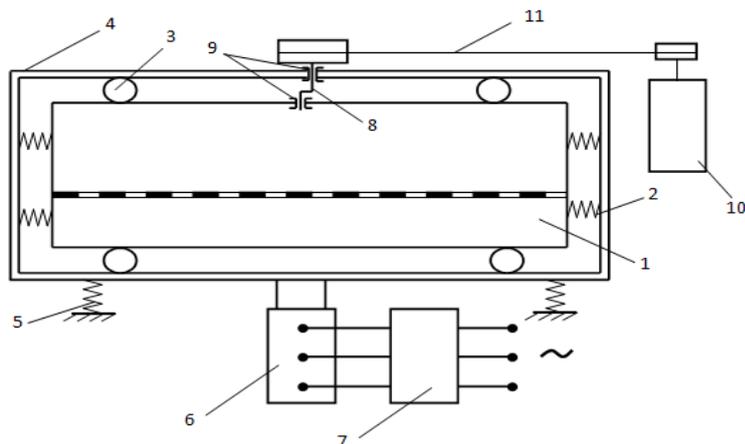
Новая конструкция вибрационного грохота: 1 - короб с просеивающей поверхностью; 2 - упругие элементы; 3 - кинематические соединения; 4 - подвижная рама; 5 - амортизатор; 6 - вибропривод; 7 - преобразователь частоты; 8 - вертикальный эксцентриковый вал; 9 - подшипники; 10 - электродвигатель; 11 - ременная передача.
